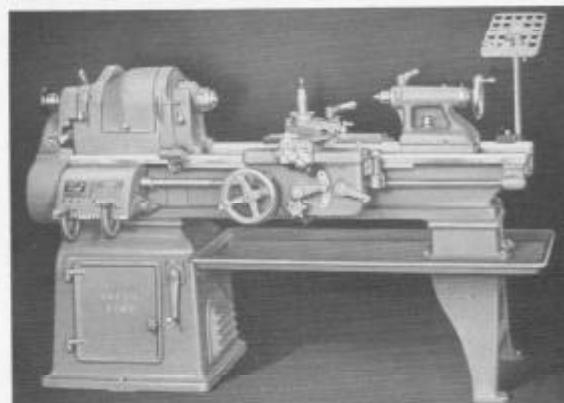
Torno moderno para taller con transmisión por motor debajo del cabezal
